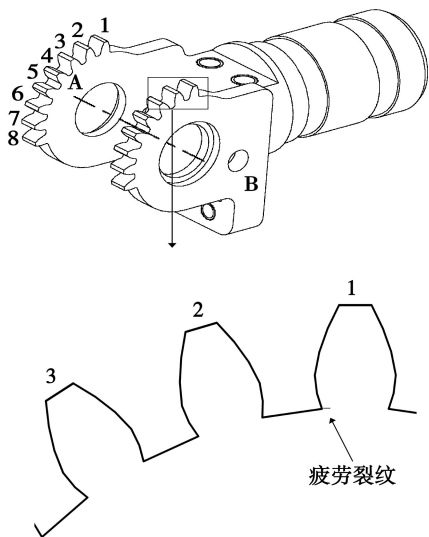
齿轮 B 齿 1 的疲劳裂纹位置示意图
